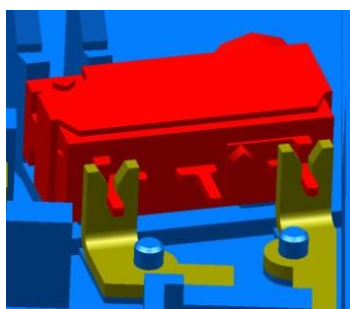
Detail oblasti pro spojení odporovým svařováním
